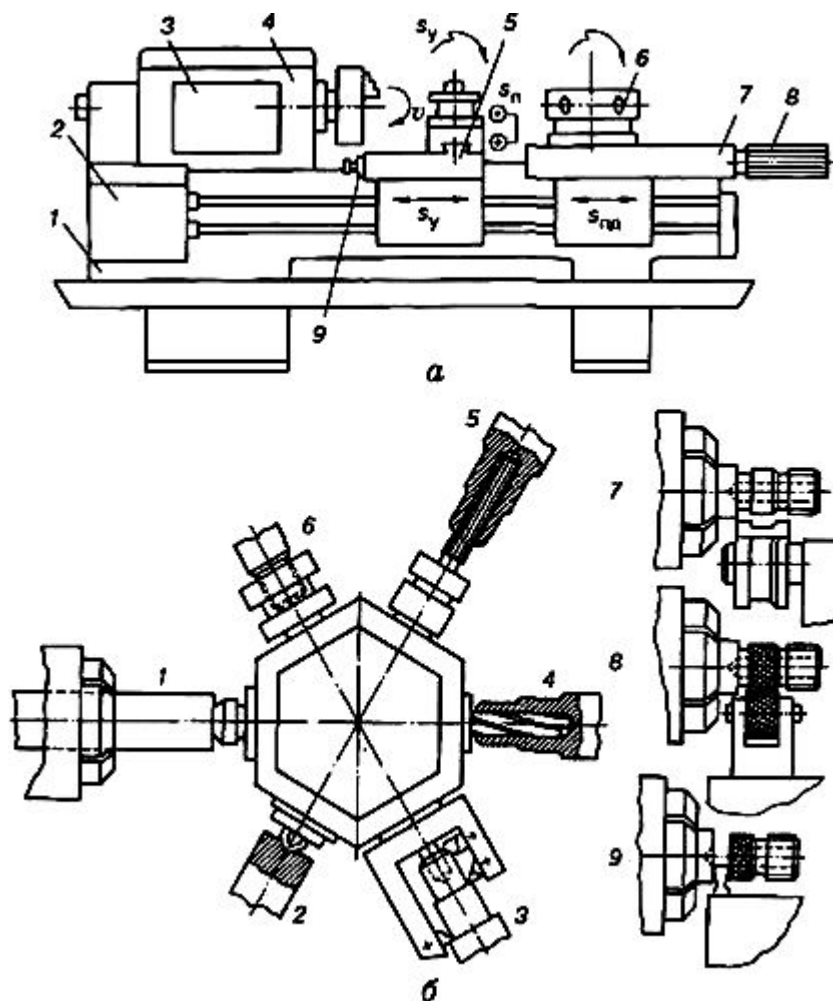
Токарно-револьверний верстат з вертикальною віссю револьверної головки: а – загальний вигляд; б – схема налагодження верстата для обробки втулки
